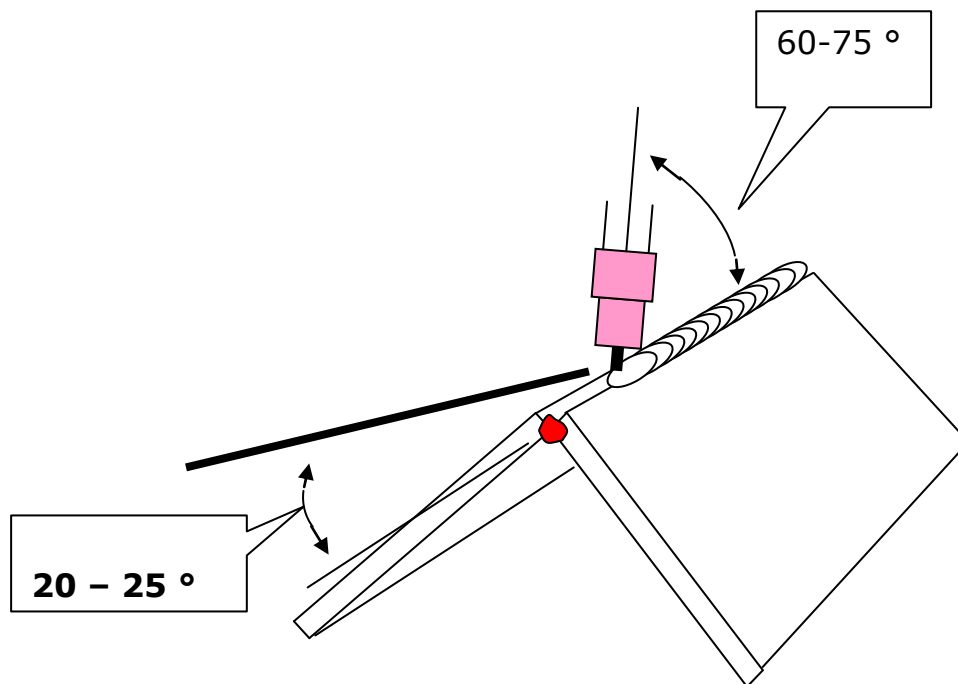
Realización de la soldadura en junta de esquina en posición plana con aporte.
